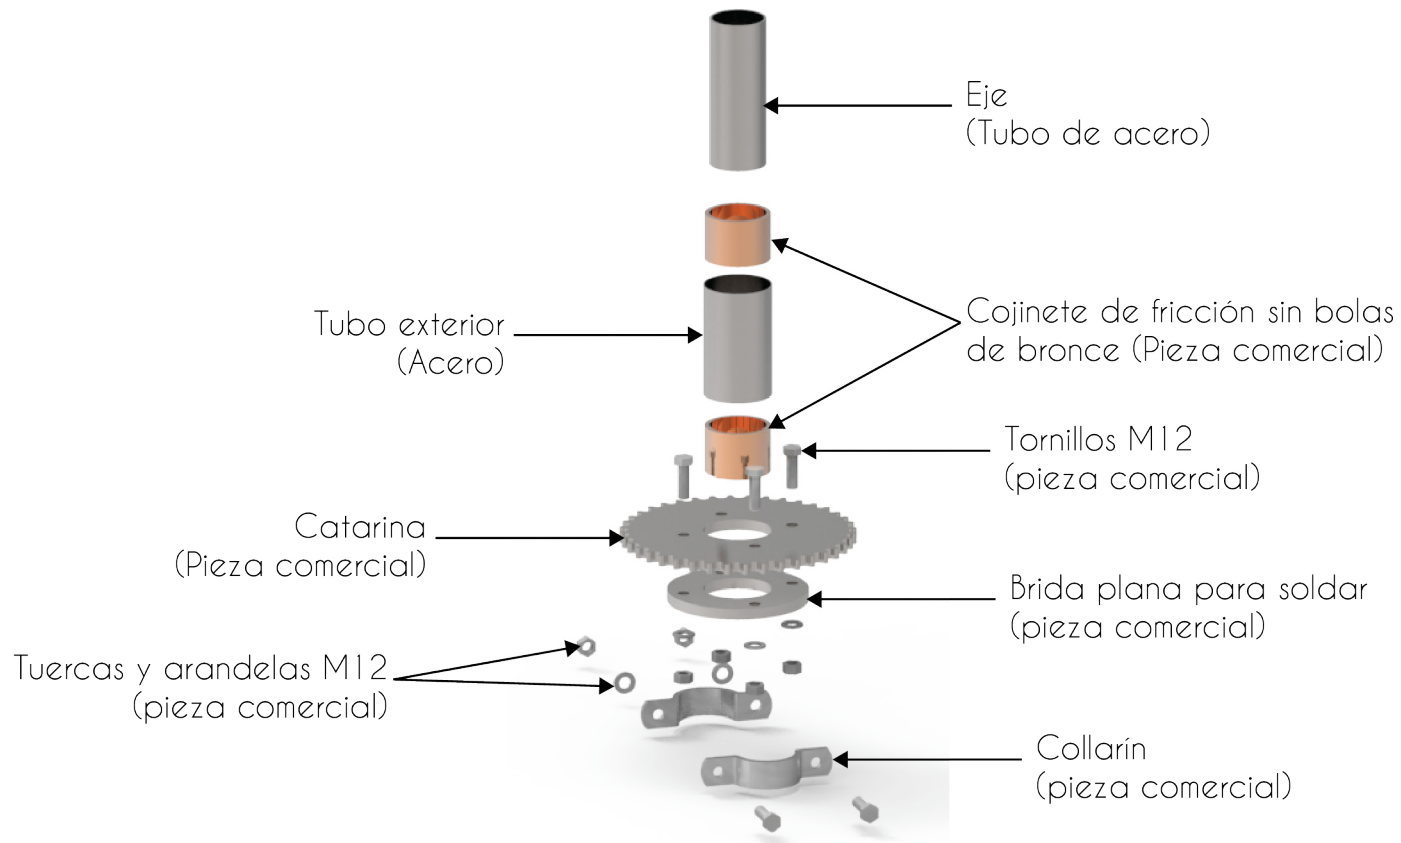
Explosiva mecanismo de giro del juego "Tornado"
